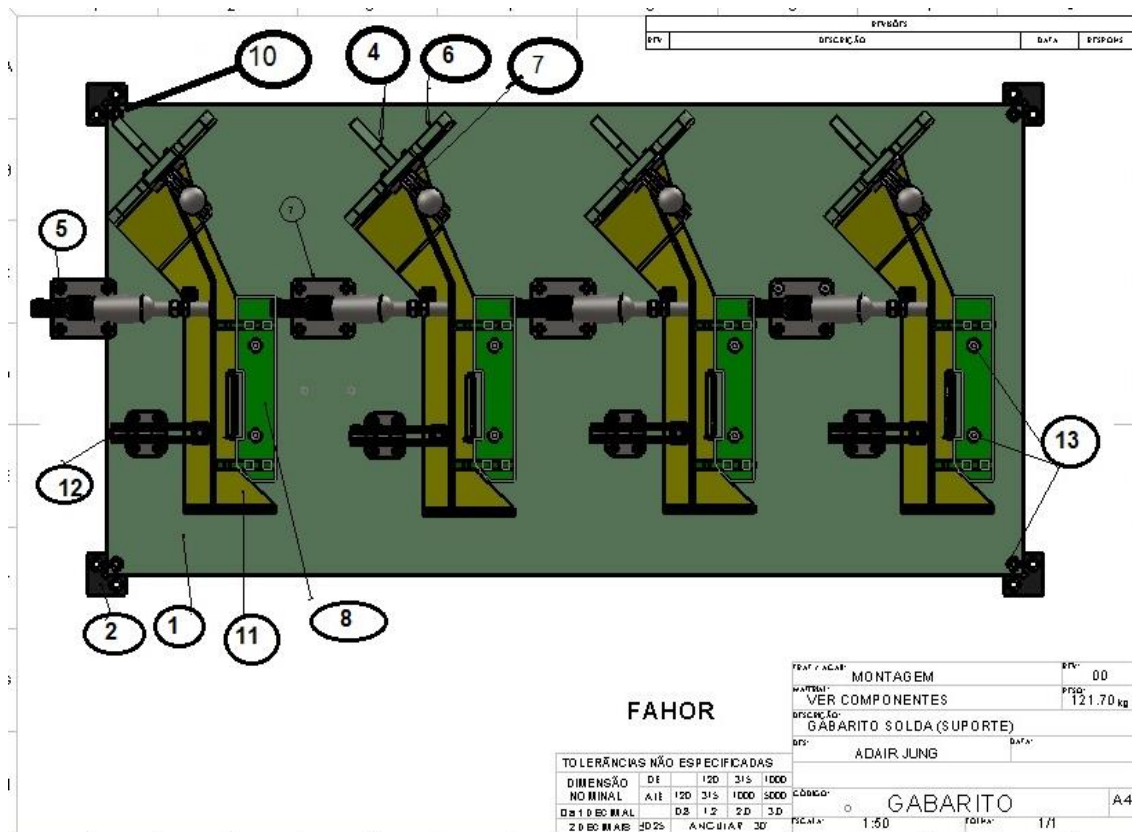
Esboço final do dispositivo de fixação para soldagem.
